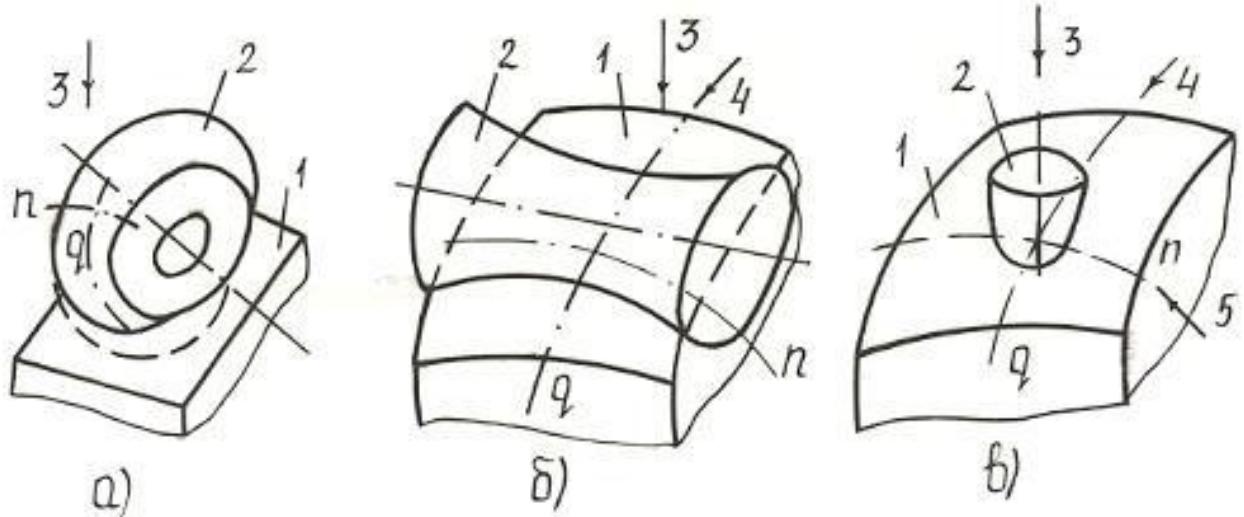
Способы формообразования номинальной поверхности детали: n, q – образующая и направляющая линии номинальной поверхности 1; 2 – производящая (ИИП) поверхность инструмента; 3 – подача сближения; 4, 5 – формообразующие подачи
